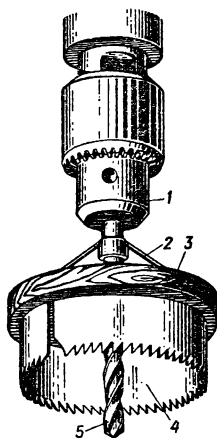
Приспособление для сверления отверстий большого диаметра:
